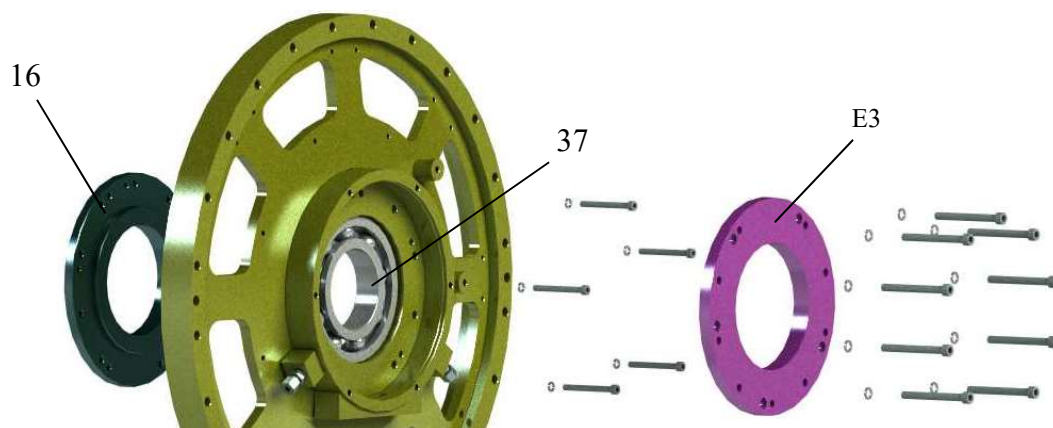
Установка внутреннего лабиринта в подшипниковый щит со стороны привода
